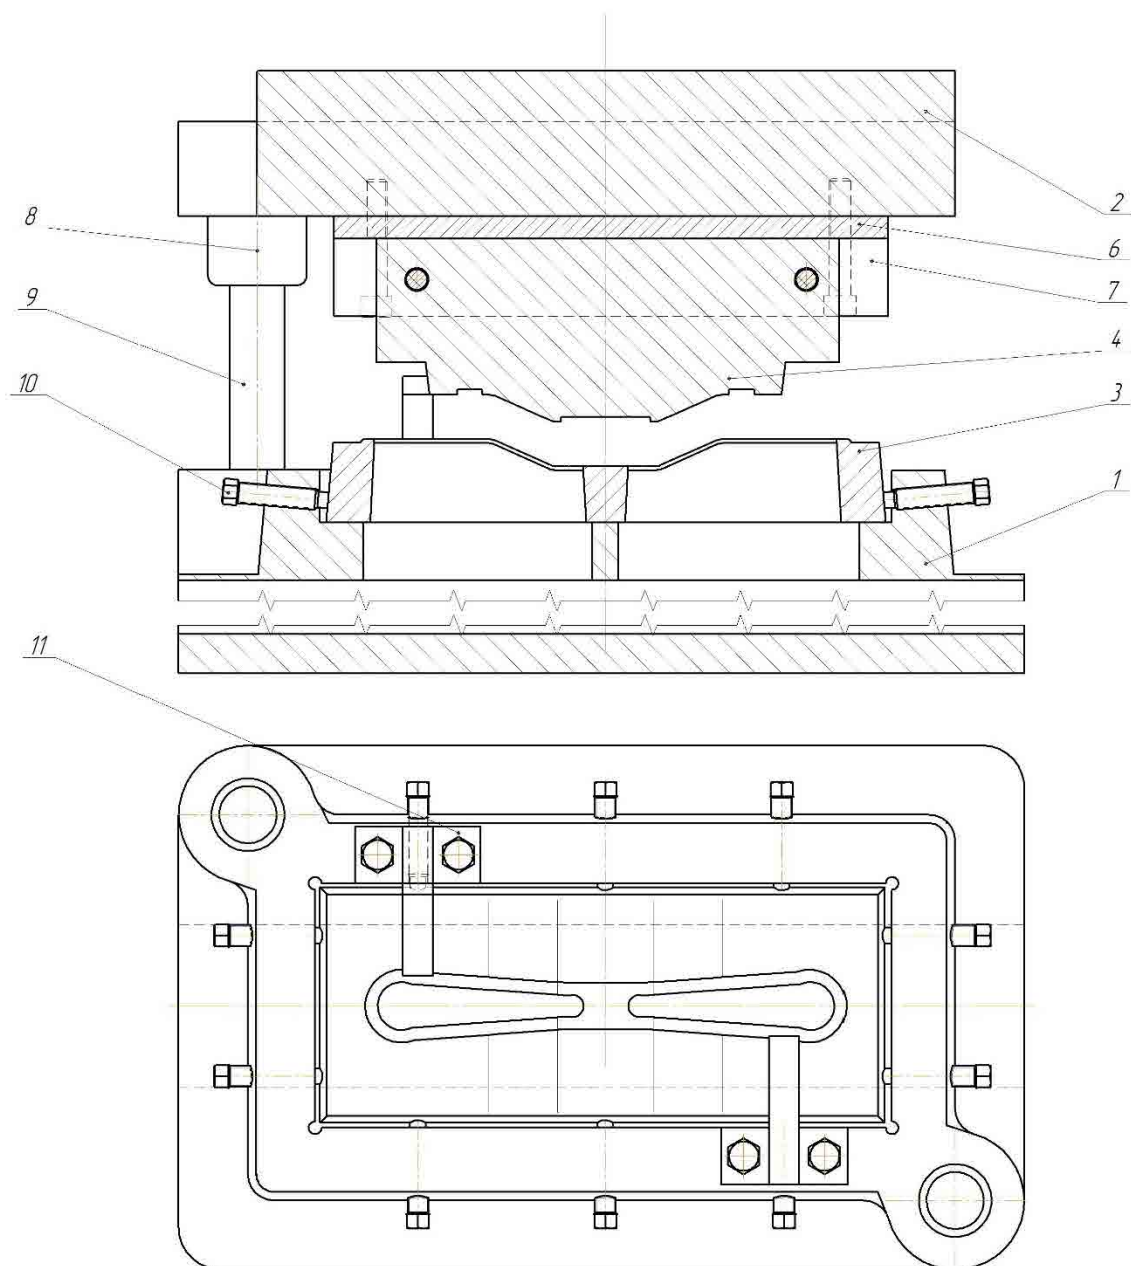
Загальний вигляд обрізувального штамп
